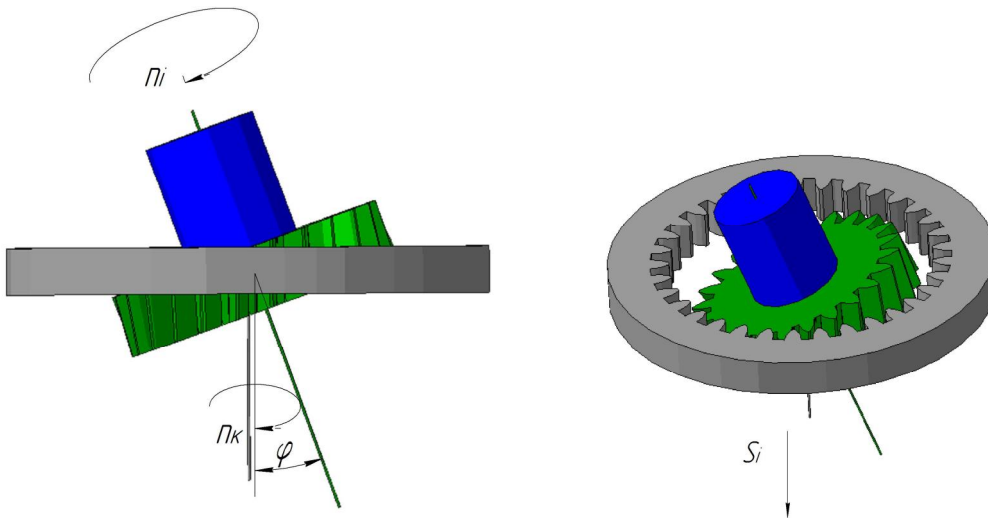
Схематичне розташування інструменту та заготовки при обробці Power Skiving
